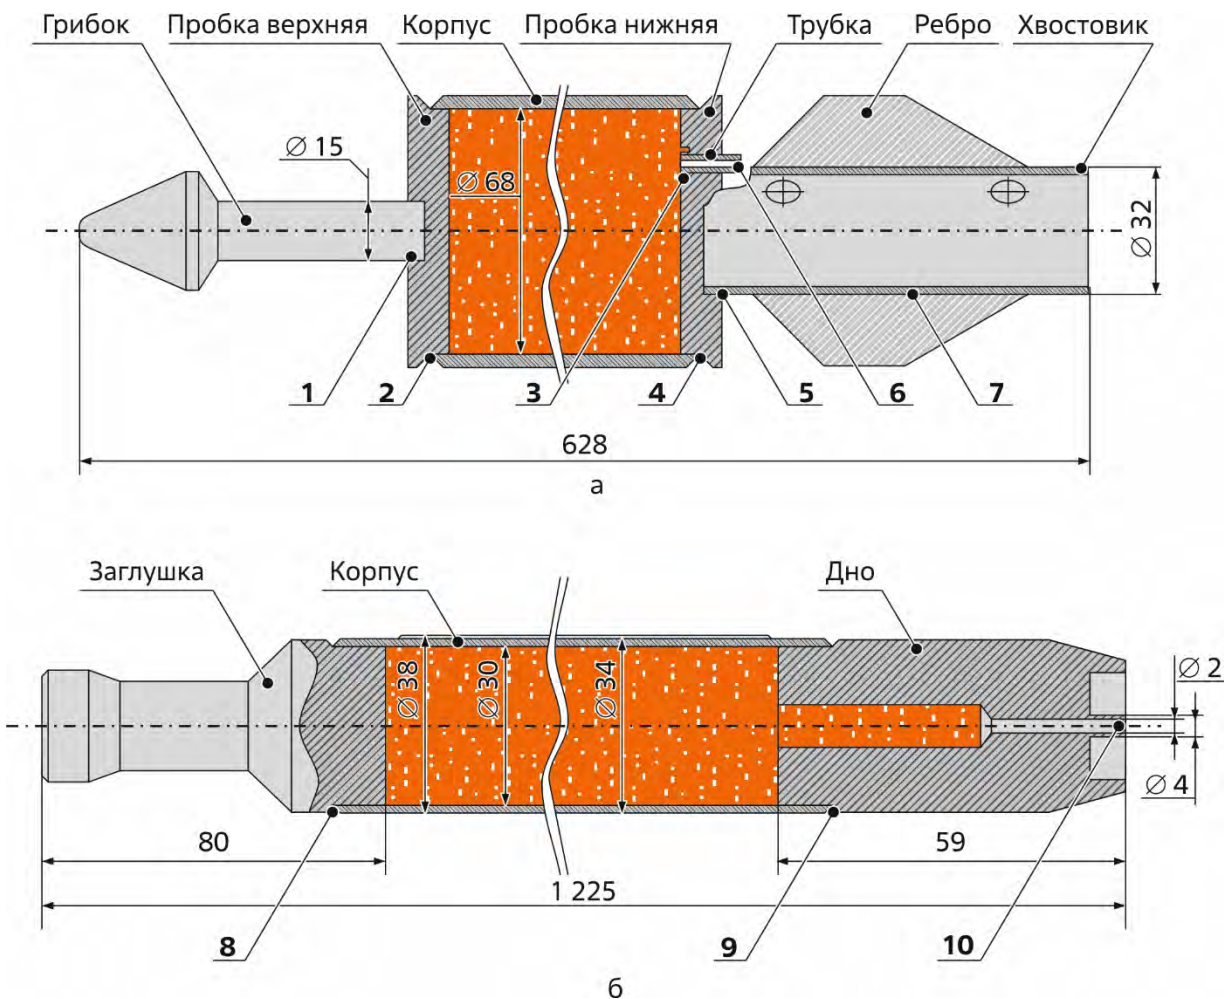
Эскиз облучательного устройства для наработки изотопа в реакторах СМ (а) и МИР (б) с указанием номеров сварных швов
